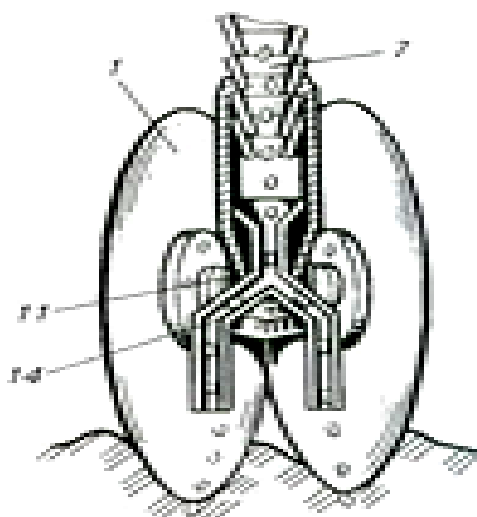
Вид двухдискового двухстрочного сошника
